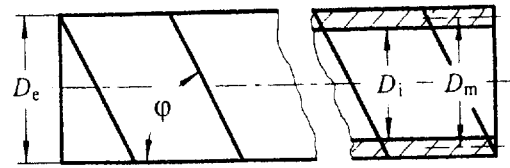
Tuyau soudé hélicoïdalement
